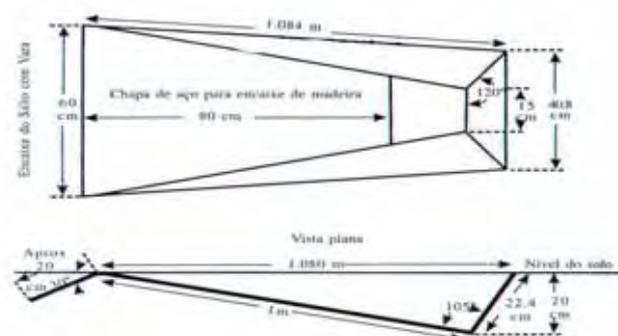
Vista superior e lateral da caixa metálica do encaixe.
